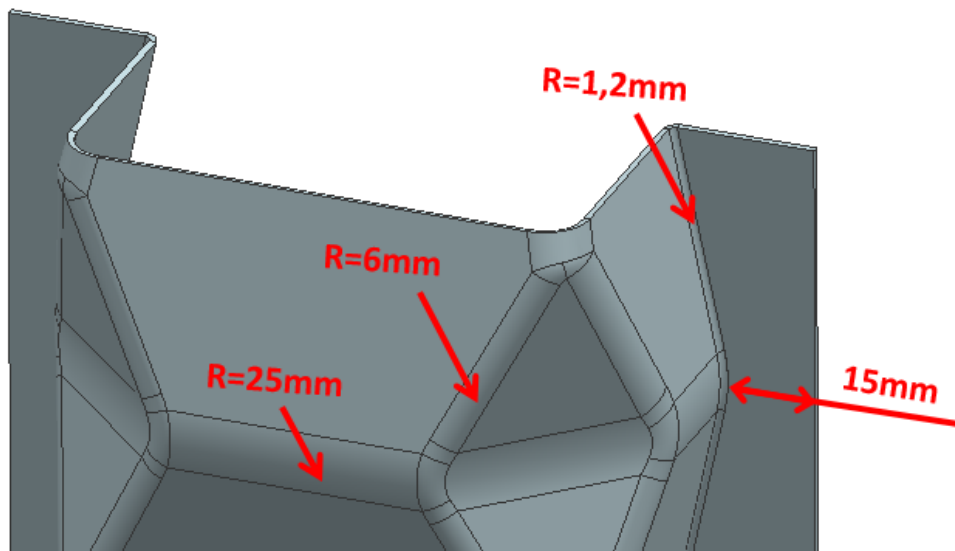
Detalhamento geometria origami crash box origami para soldagem RSW
